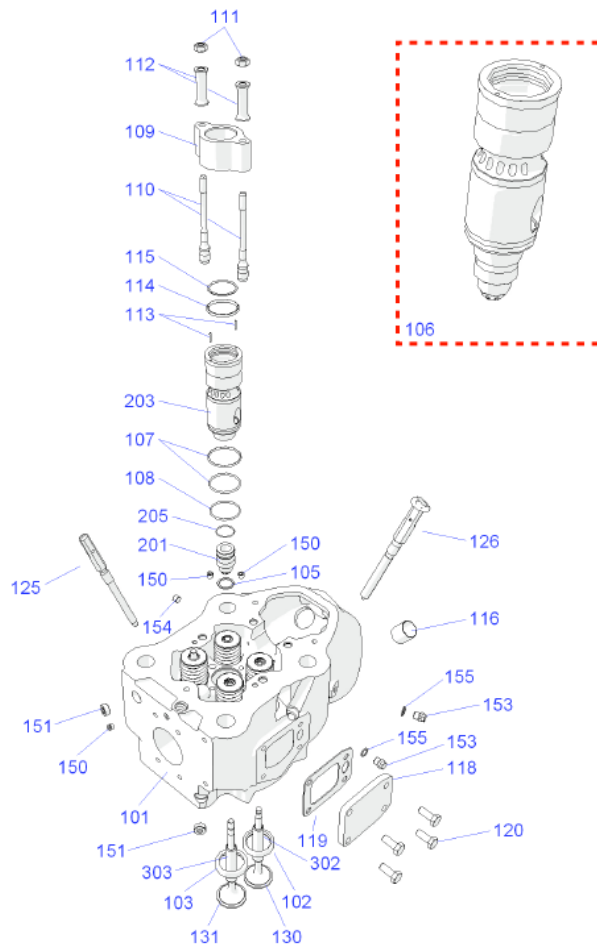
Explosionszeichnung Zylinderkopf⁸⁴
